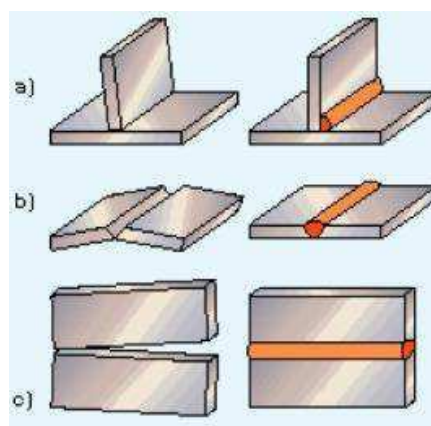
Pré-deformação de a) junta de filete, b) junta de topo, c) pré-rotação em junta de topo. (TWI,2014).
